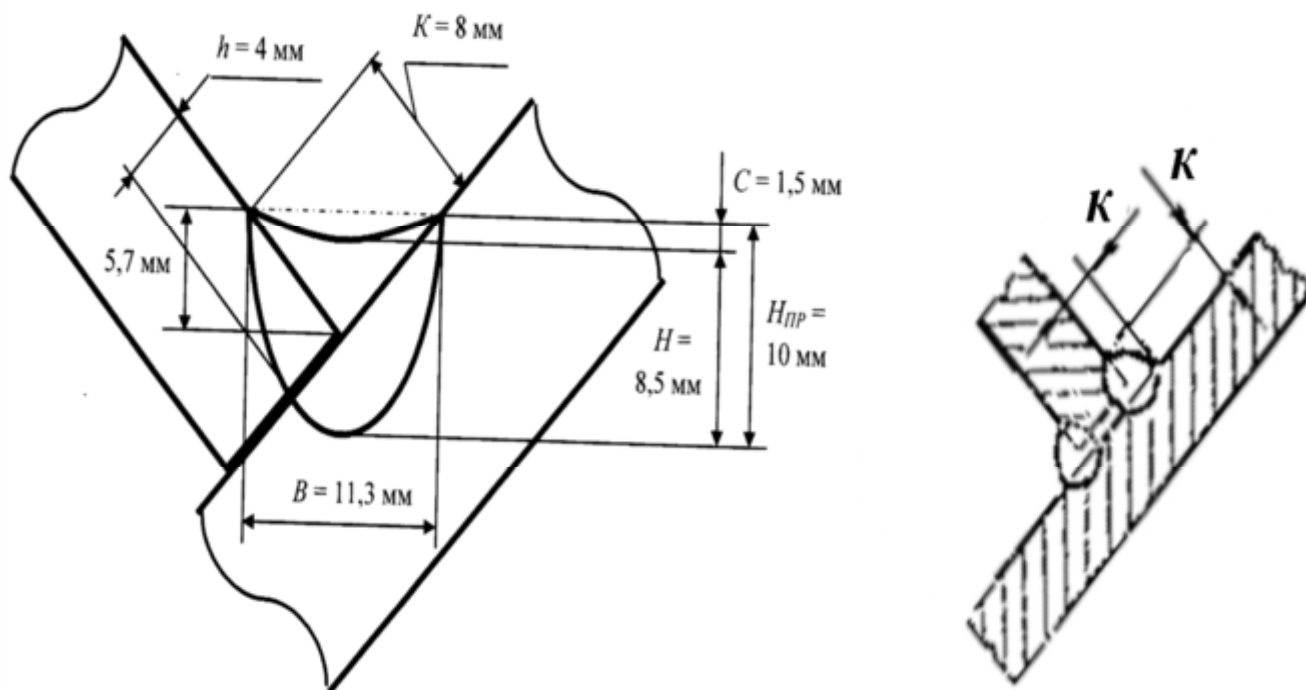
Схема сварного соединения ТЗ
